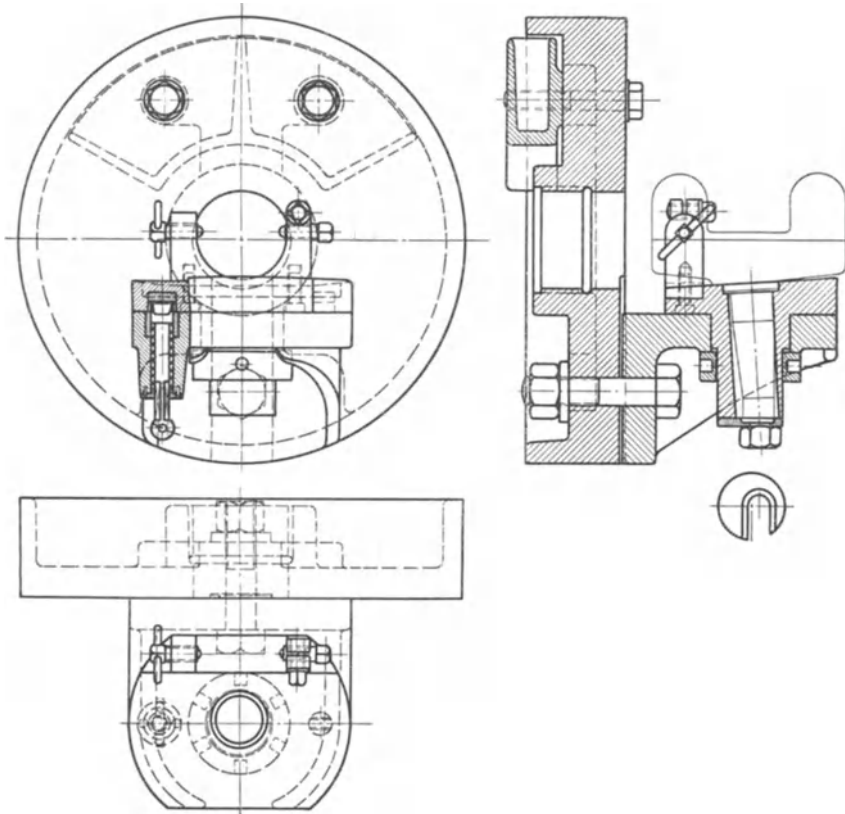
Vorrichtung für Dreh- oder Revolverbankarbeiten für Bearbeitung von zwei Seiten.
